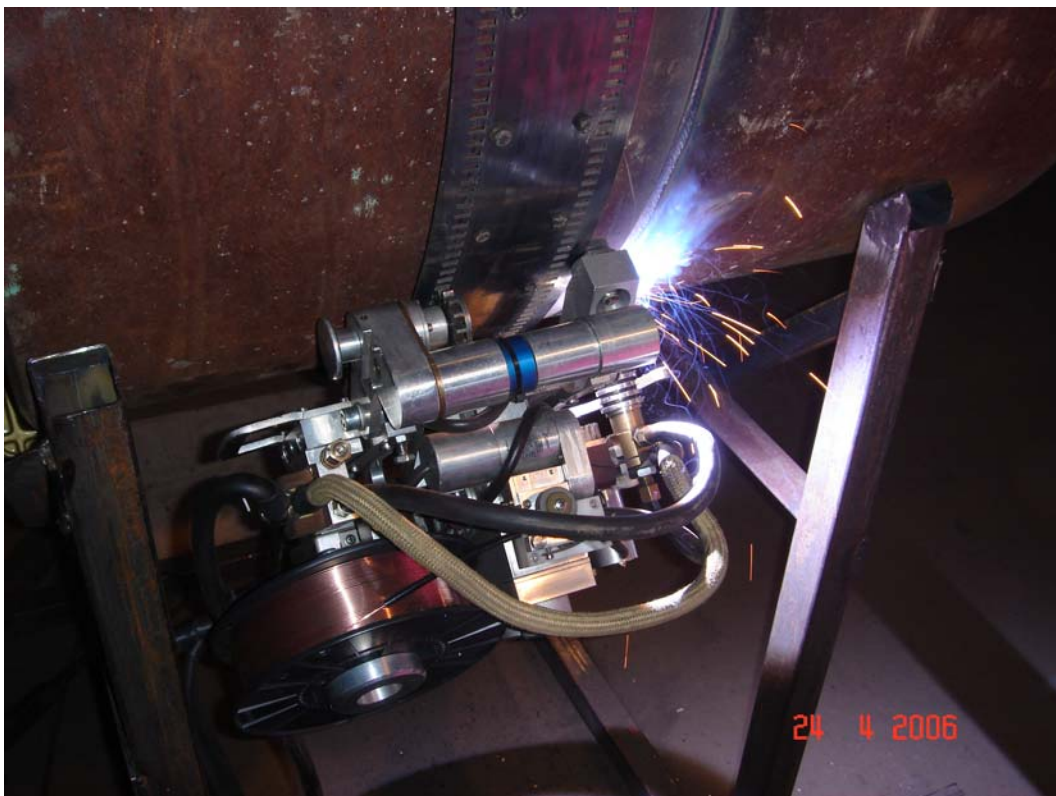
Вид сварочного процесса на головке ПРОТЕУС.
